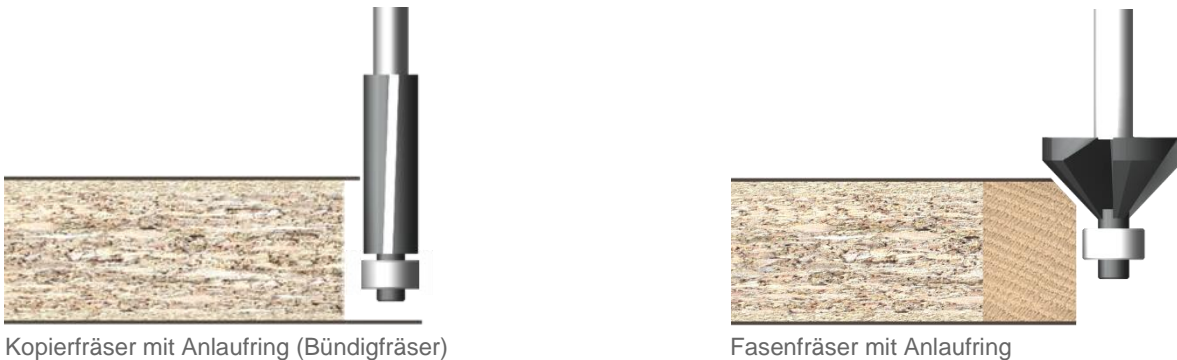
Beispiele für Fräsworkzeuge für Handmaschinen
